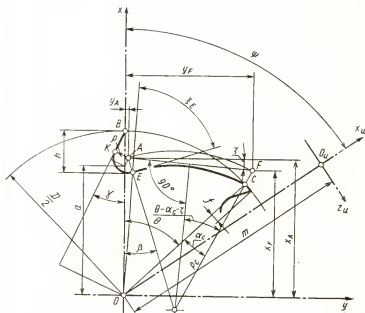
Профиль винтовой канавки цилиндрической фрезы с крупным зубом
